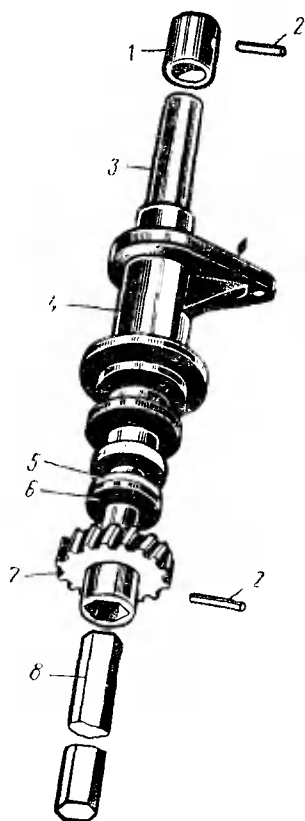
Привод прерывателя-распределителя двигателя ЗМЗ-53:
